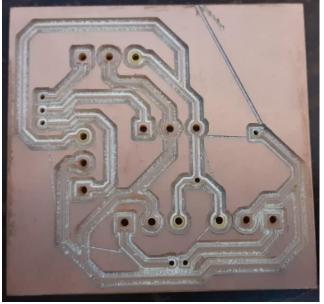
PCB 1 que sofreu com defeitos da prototipadora
